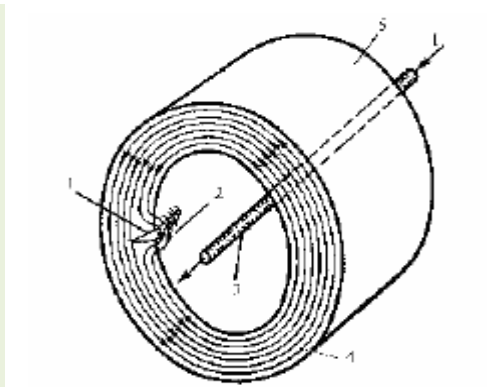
Схема циркулярного намагничивания детали пропусканием тока по стержню:
